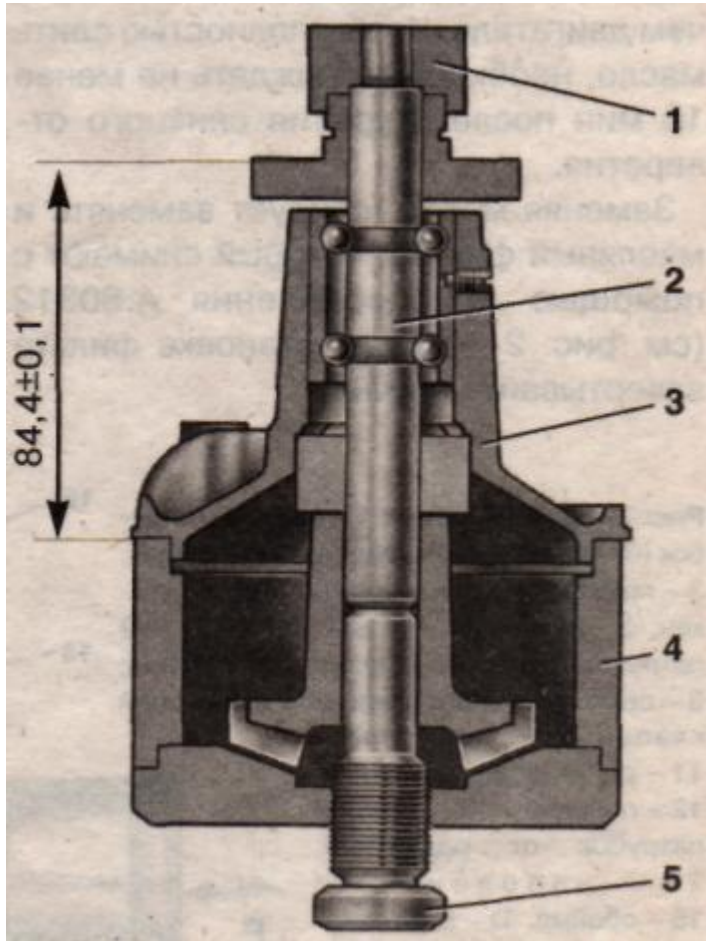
Напрессовка крильчатки на валик насоса пристосуванням А.60430: 1 - опора; 2 - валик насоса; 3 - кришка корпусу насоса; 4 - склянка; 5 - становлюючий гвинт
